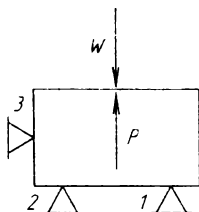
Схема установки, при которой силы резания стремятся оторвать заготовку от опор
